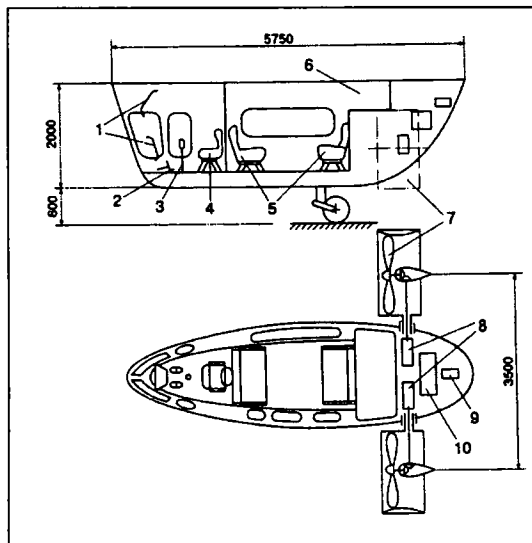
Компоновка гондолы дирижабля ДП-200: 1 — приборные доски; 2 — педали управления по курсу; 3 — ручка управления рулями высоты; 4 — кресло пилота; 5 — пассажирские двухместные диваны; 6 — ниша для укладки багажа; 7 — поворотные винтокольцевые движители; 8 — двигатели; 9 — автономный источник питания; 10 — топливный бак на 200 л
